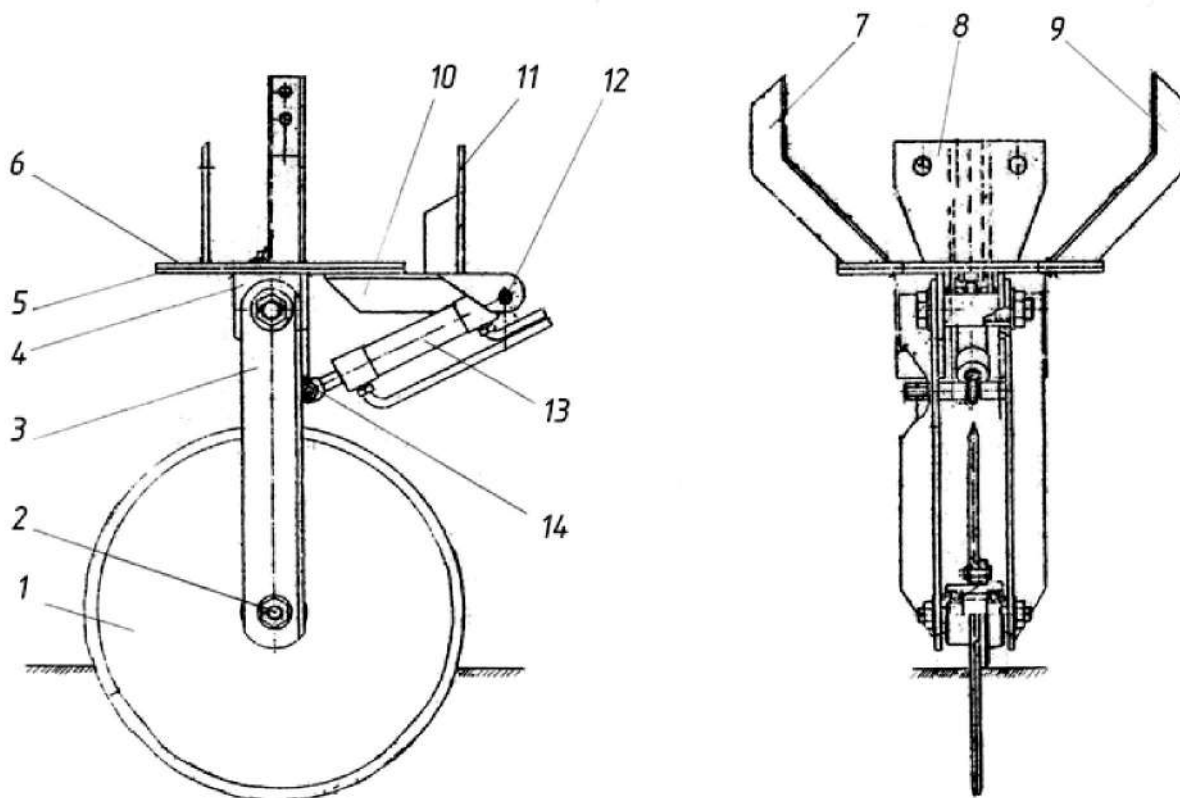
Стабилизатор прямолинейного движения трактора:
